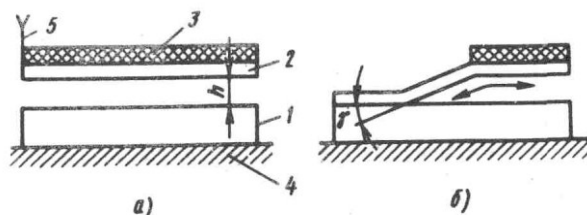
Сварка взрывом: 1, 2 — свариваемые пластины; 3 — заряд В.В.; 4 — основание; 5 — детонатор
